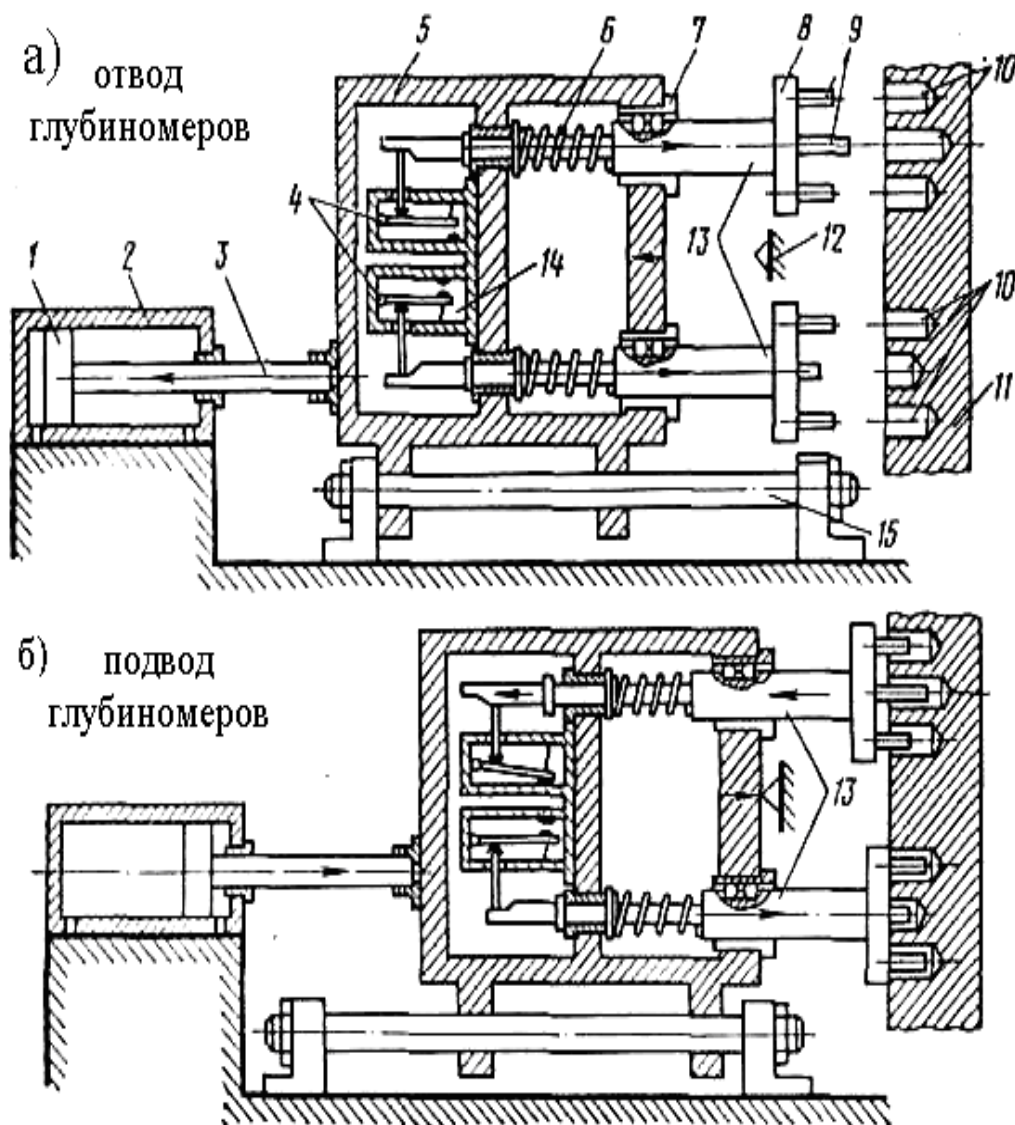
Контрольное приспособление для проверки глубины просверленных отверстий в корпусных деталях:
